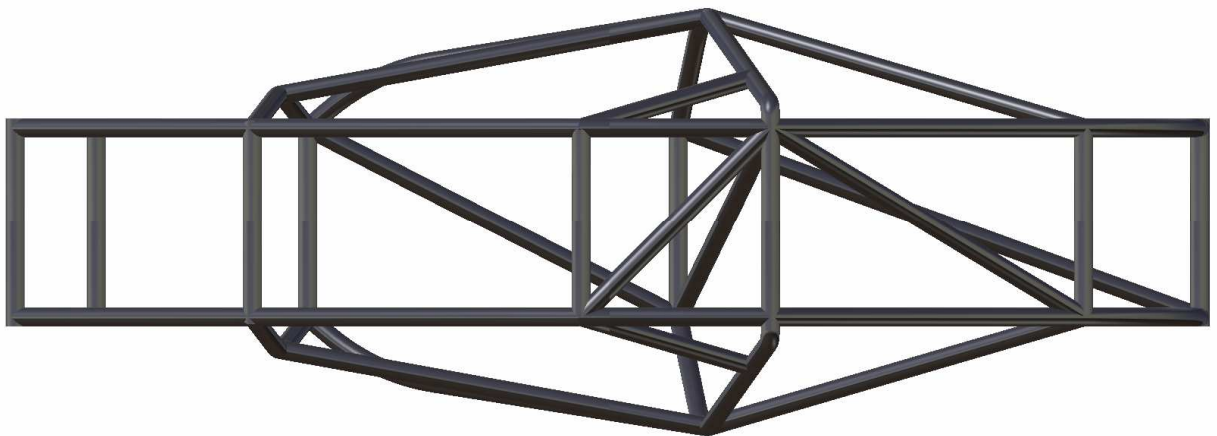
Vista en planta del chasis. Fuente: elaboración propia.
